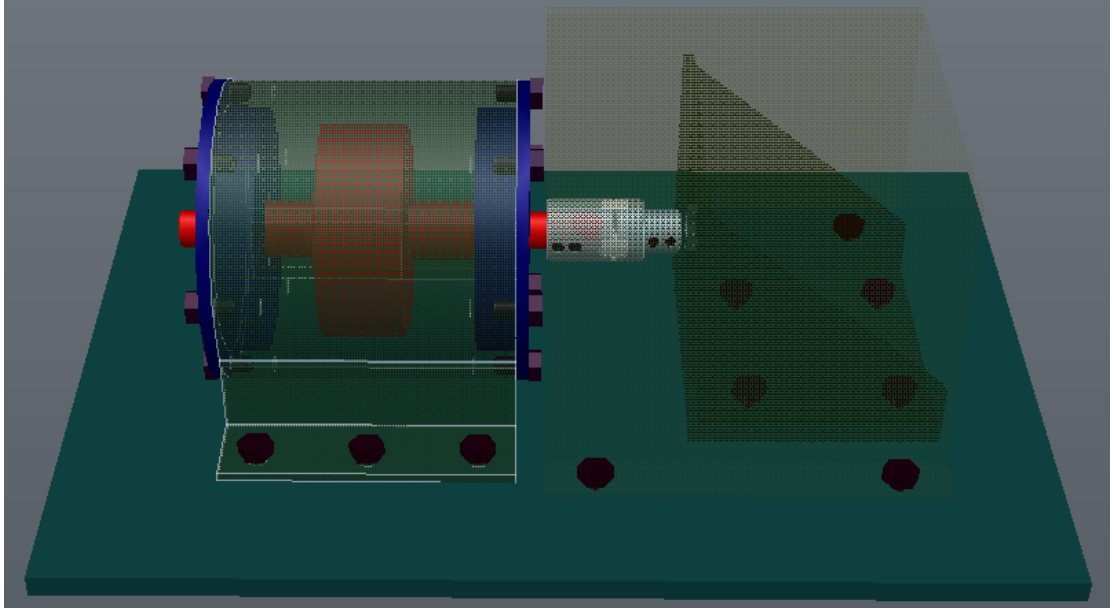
Ön testlerde kullanılan M/G sürücü ünitesi [54]
